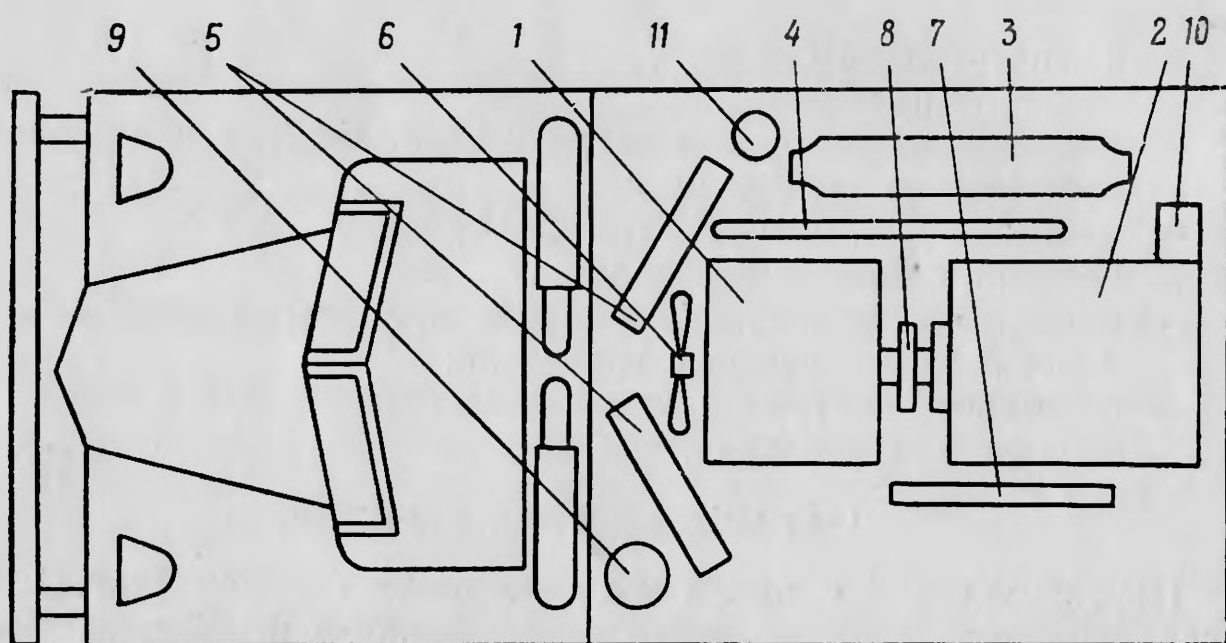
Схема расположения основных агрегатов компрессорной станции:
